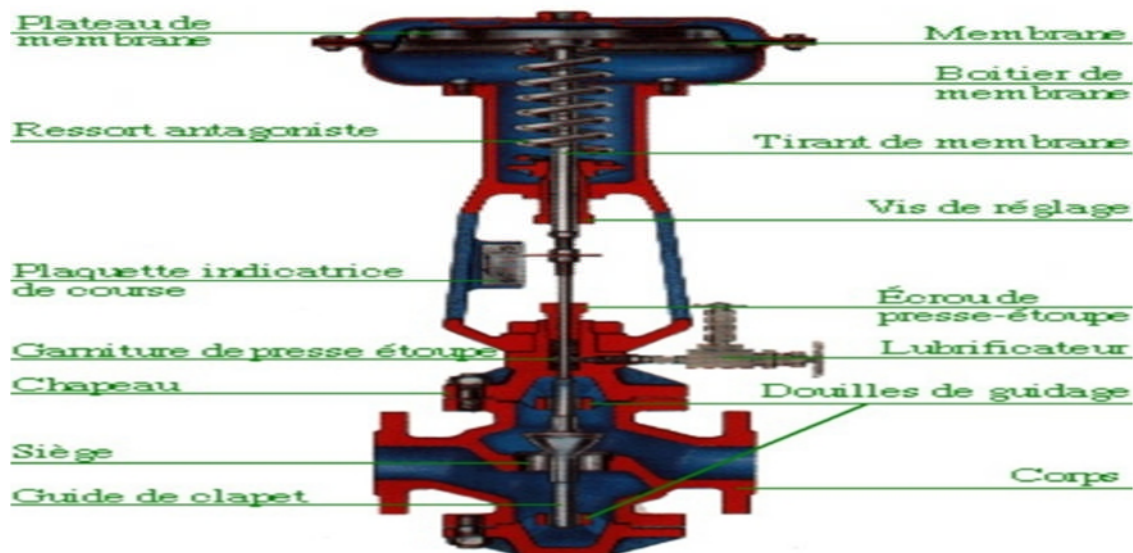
Vue en coupe d'une vanne de régulation pneumatique
